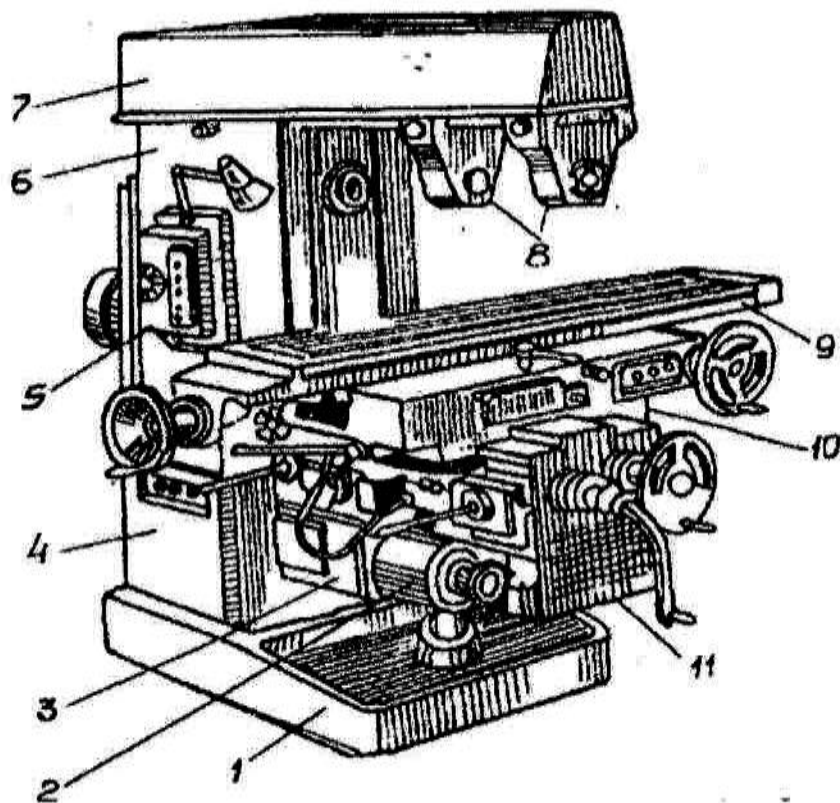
Горизонтально-фрезерный станок: 1 -фундаментальная плита; 2-механизм переключения подач; 3-коробка подач; 4-крышка с электроаппаратурой; 5-механизм управления коробкой скоростей; 6-станина; 7-хобот; 8-кронштейн; 9-продольный стол; 10-салазки; 11-консоль
